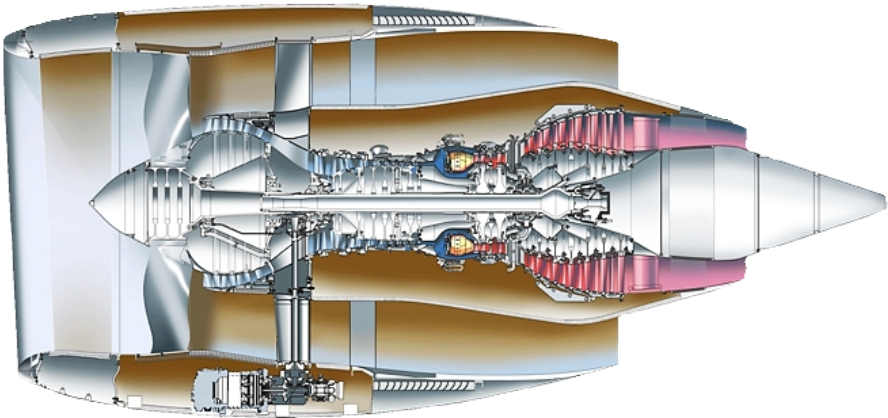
Внешний вид турбореактивного двухконтурного двигателя ПД-14
